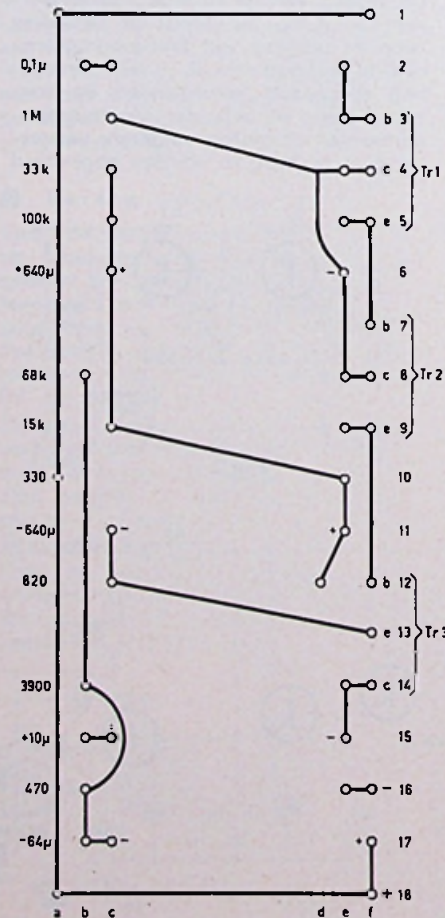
PLAN VOOR EEN EENVOUDIGE GEDRUKTE BEDRADING VOOR DE EERSTE VOORVERSTERKER (NIET OP SCHAAL)
